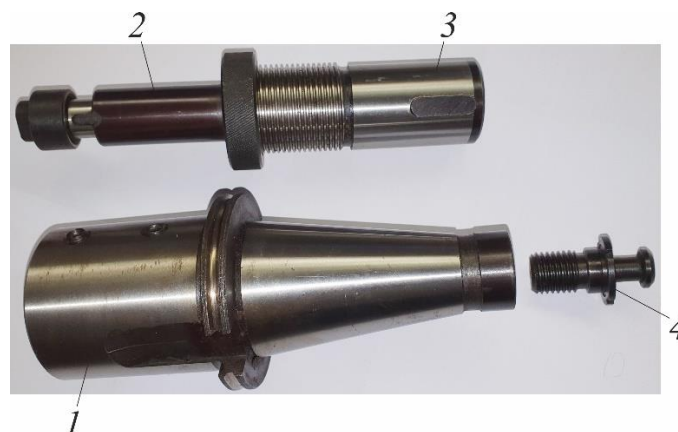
Элементы АСП для установки дисковой фрезы: 1 – базисный агрегат; 2 – рабочая часть сменного агрегата; 3 – хвостовик сменной наладки; 4 – зажимной болт
